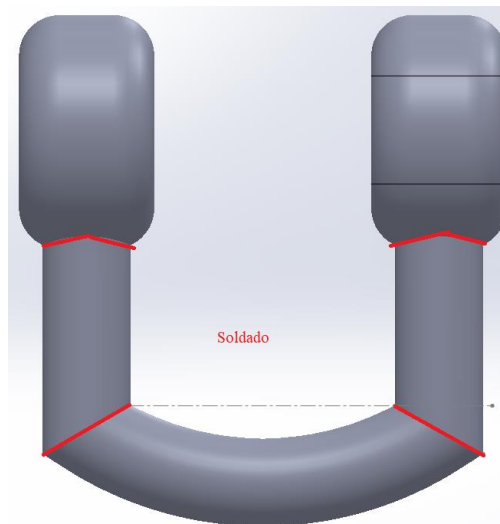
Vista de soldado de mosquetón pieza N°70 (Fuente 109)
